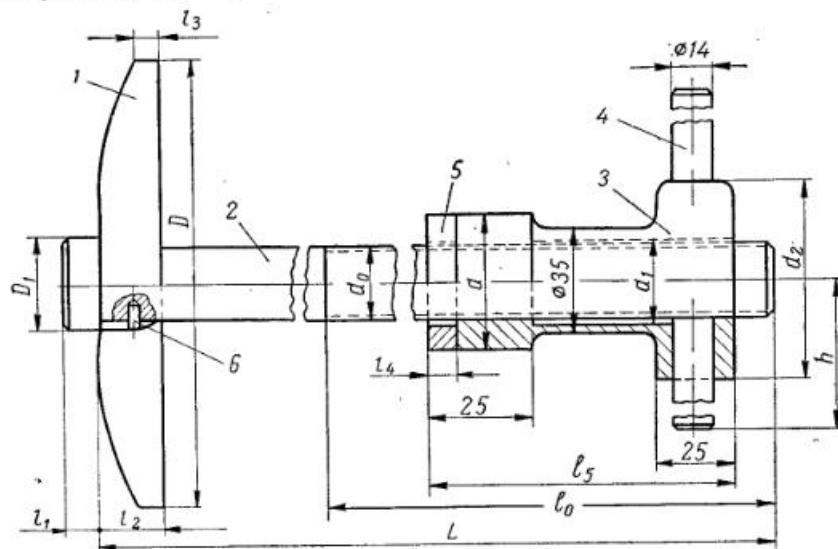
Приспособление для запрессовки направляющих втулок клапанов:
